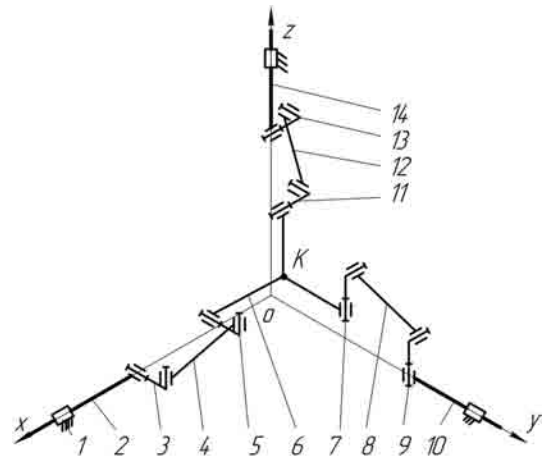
Самоустанавливающийся механизм с карданными шарнирами
